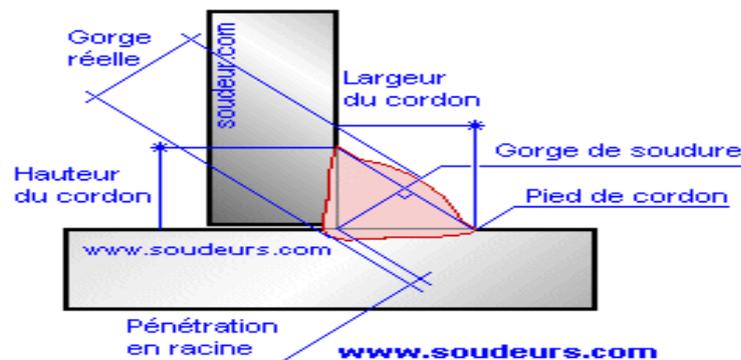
ELEMENTS DE SOUDAGE
